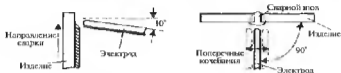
Положение электрода при сварке стыкового соединения без скоса кромок в вертикальном положении
